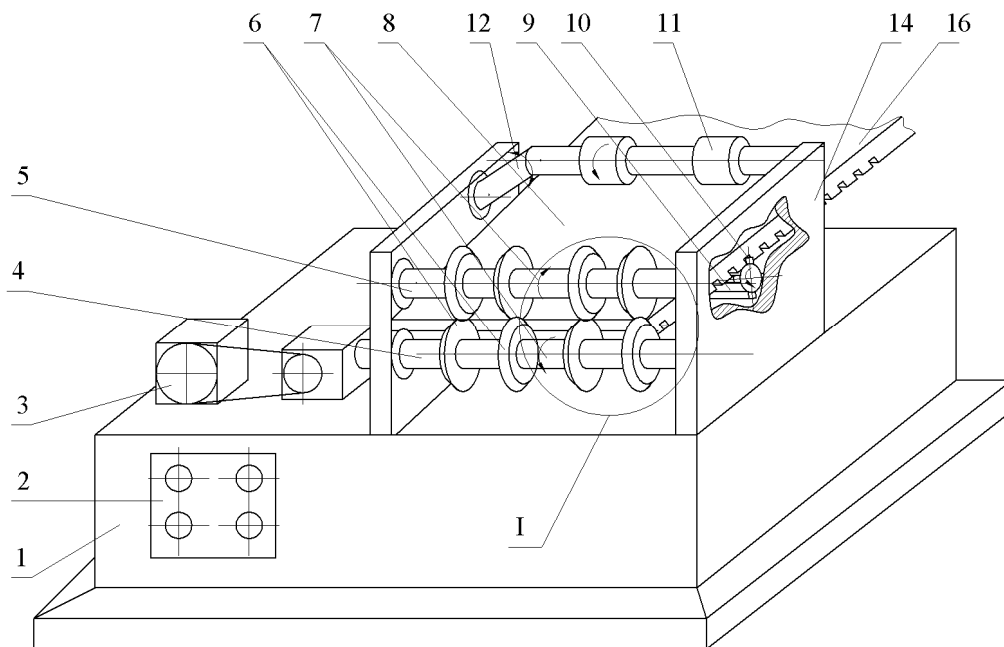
Конструктивно-компонувальна схема верстата для порізки конвеєрної стрічки.
